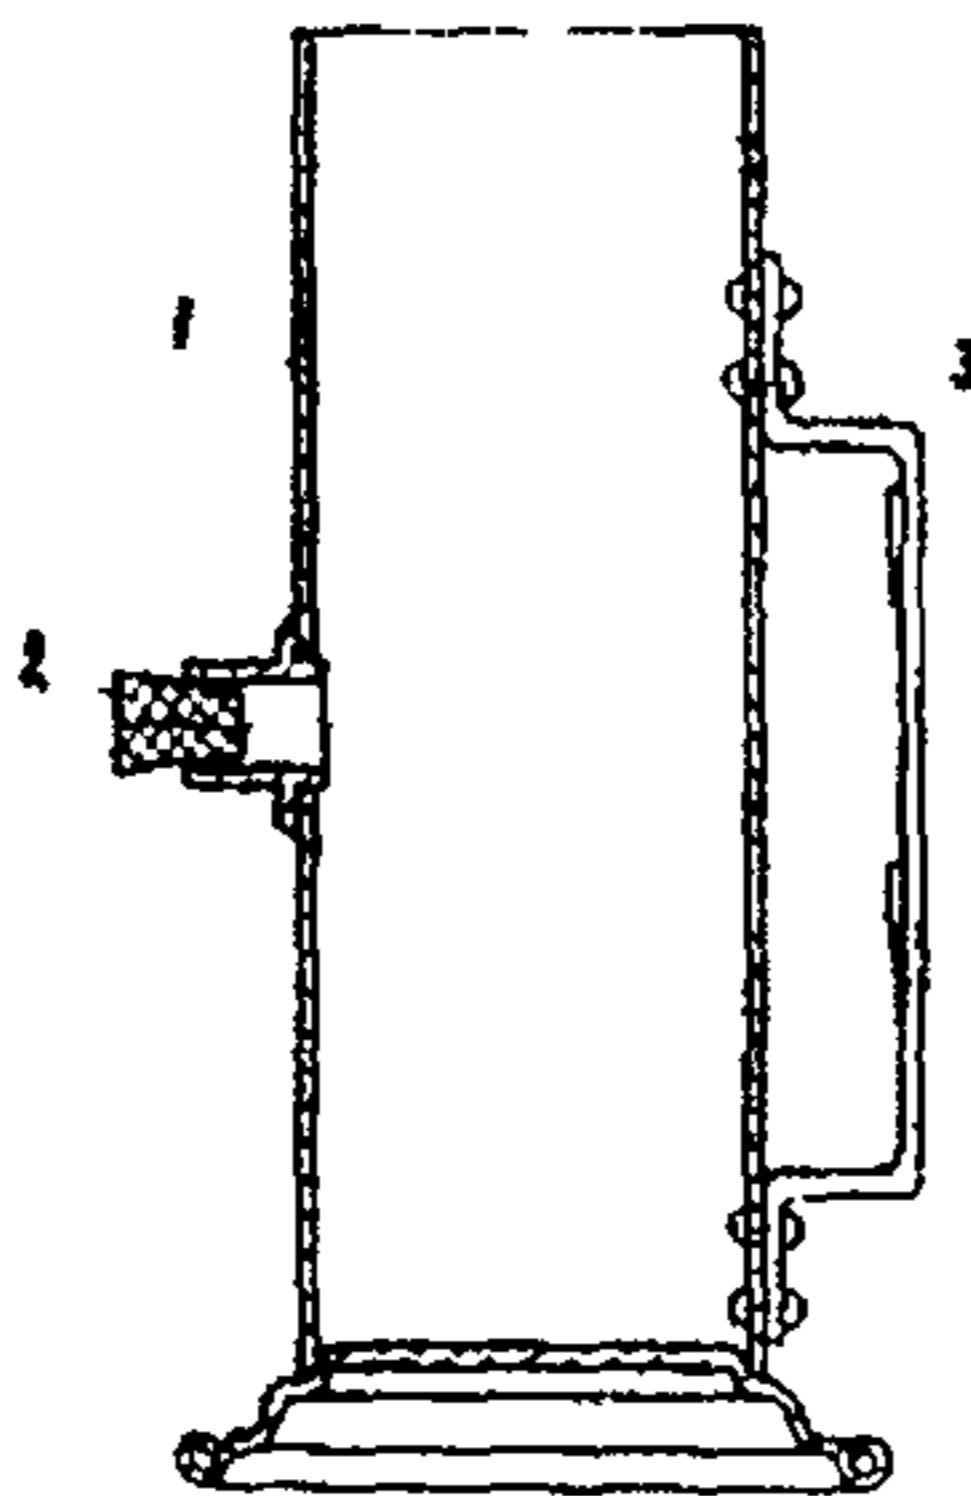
Цилиндр ЦС-2: 1 - цилиндр;
